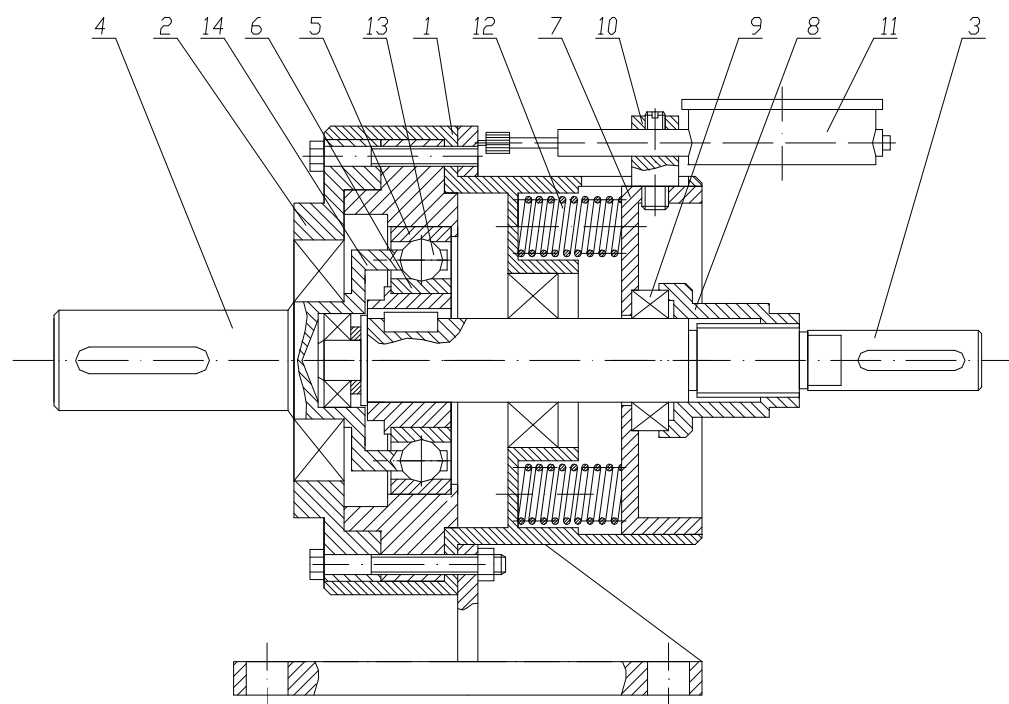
Фрикционный планетарный шарикоподшипниковый редуктор
